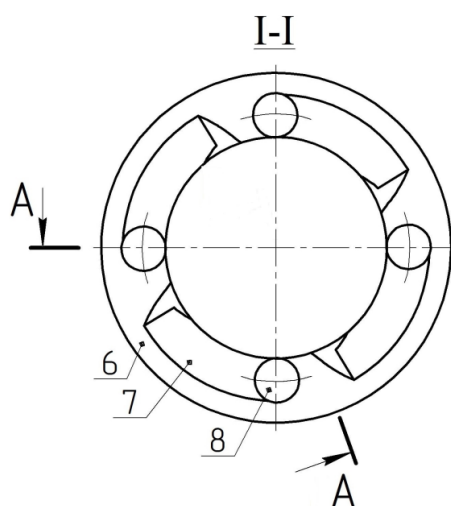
Сечение I - I рис. 49, вид по стрелкам:
